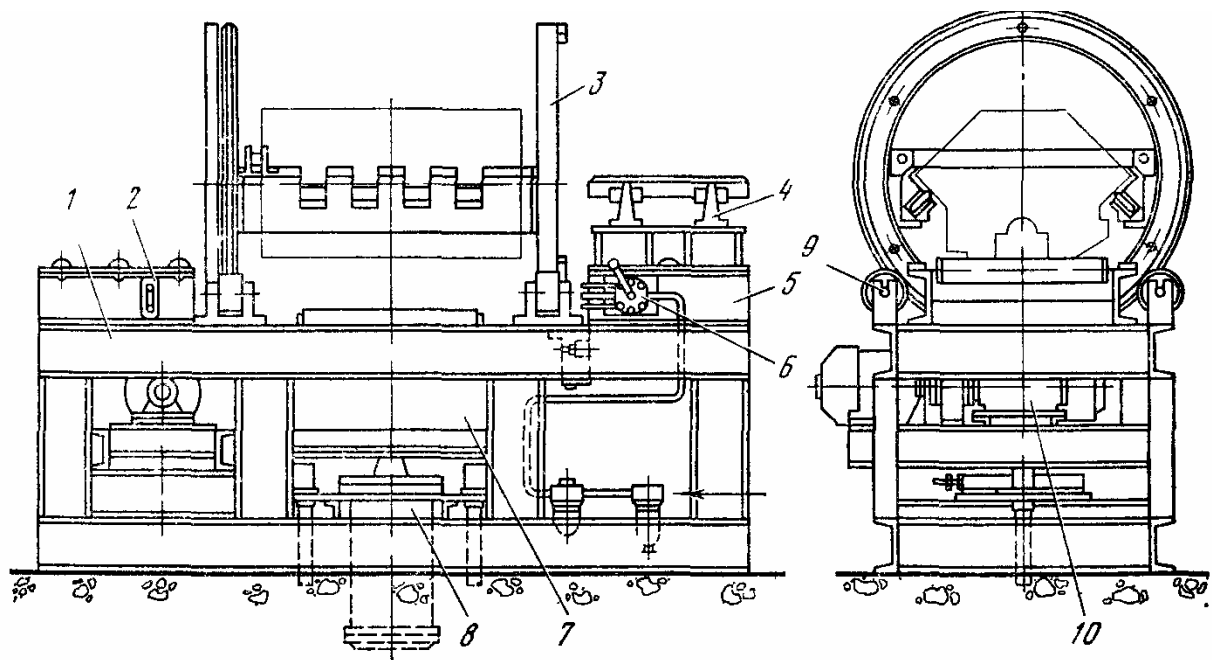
Кантователь блока цилиндров: 1 – станина; 2 и 5 – рольганги; 3 – кольцо; 4 – боковой упор; 6 – кран; 7 – подъемный стол; 8 – пневматический цилиндр; 9 – ролик; 10 – механизм поворота изделия
